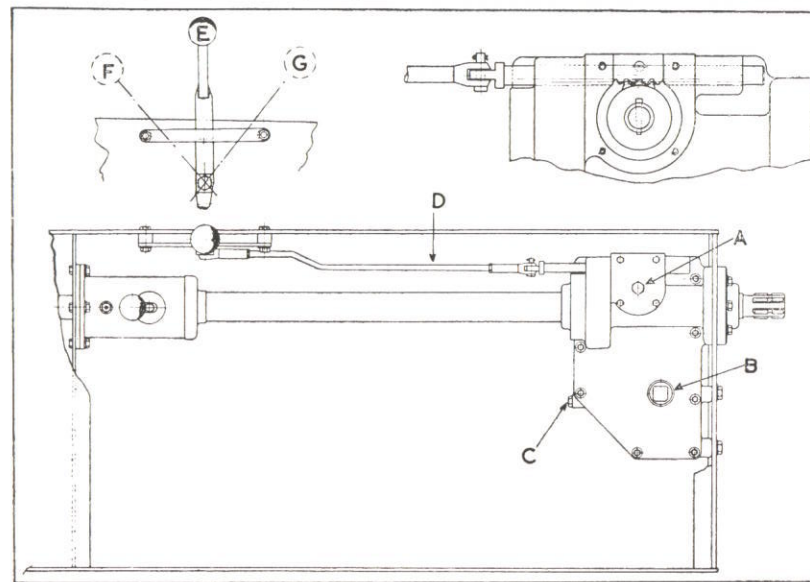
"A" vis de réglage de la soupape; "B" bouchon de remplissage d'huile; "C" bouchon de purge; "D" tringle de commande; "E" position "tenir"; "F" position "baisser"; "G" position "lever".
